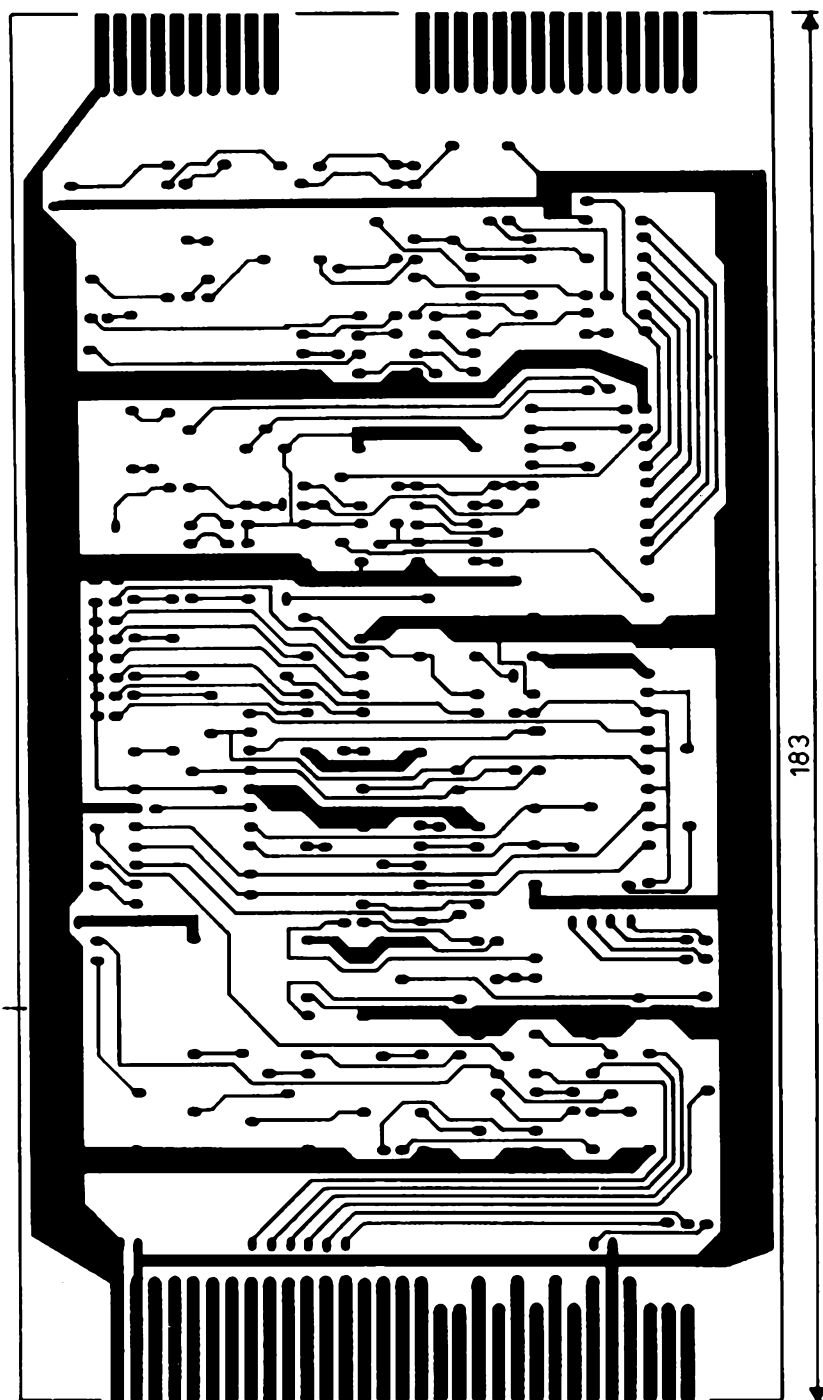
Obrazec plošných spojů desky Z506 - strana bez součástek
